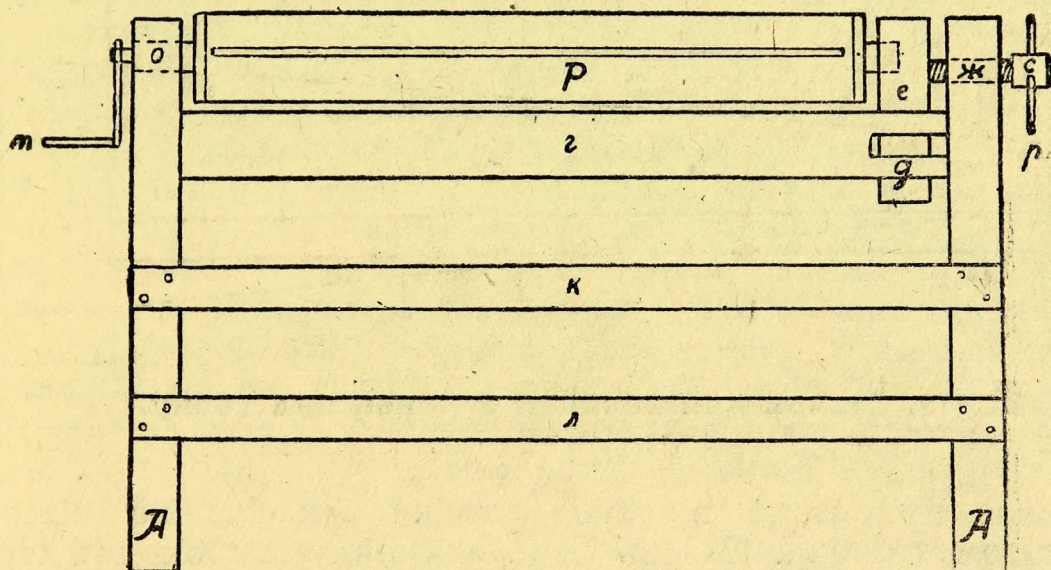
Станок для навивки основы, вид со стороны навоя.
